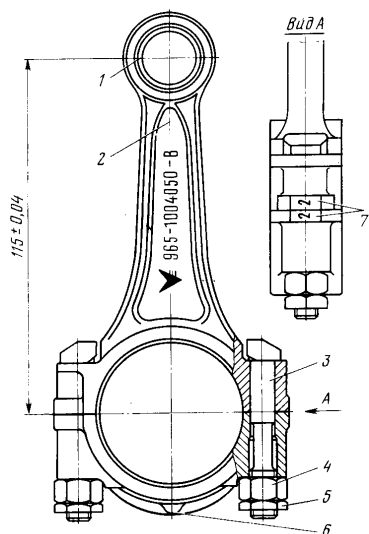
Шатун в сборе: 1 — стык втулки верхней головки шатуна; 2 — место цветного индекса размерной группы верхней головки шатуна; 3 — болт крепления крышки шатуна; 4 — гайка болта крышки шатуна; 5 — стопорная гайка; 6 — место цветного индекса весовой группы; 7 — клеймо номера цилиндра
